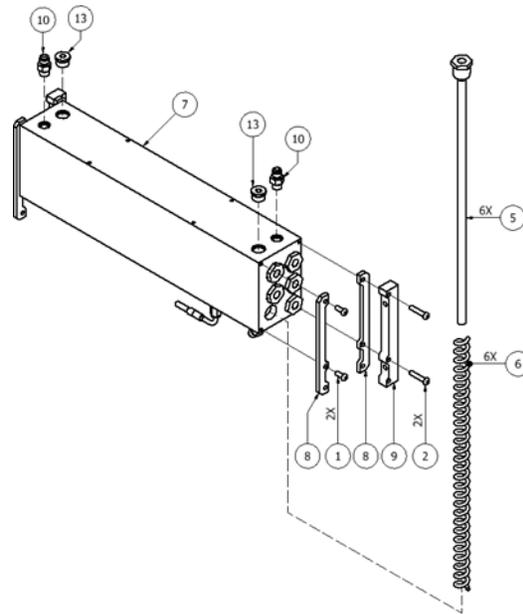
Ensamblaje del calentador, 6 varillas - A
